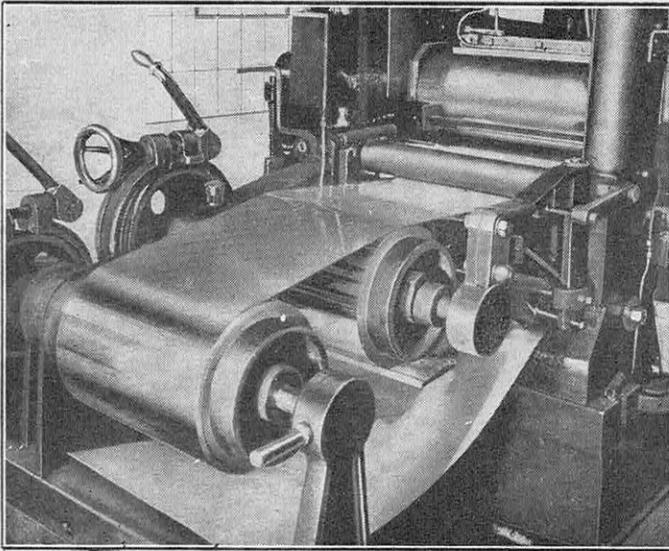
MACHINE A PRÉPARER LE PAPIER D'ALUMINIUM
